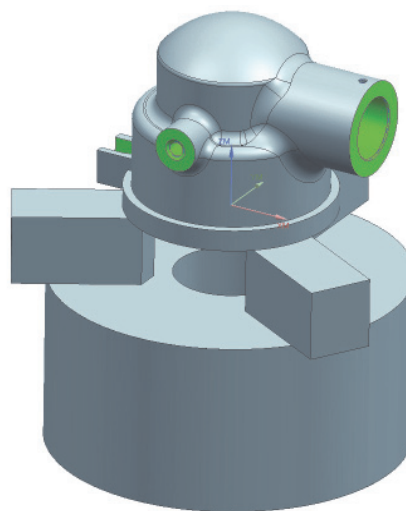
Схема установки корпусной детали при фрезеровании с традиционной схемой базирования
